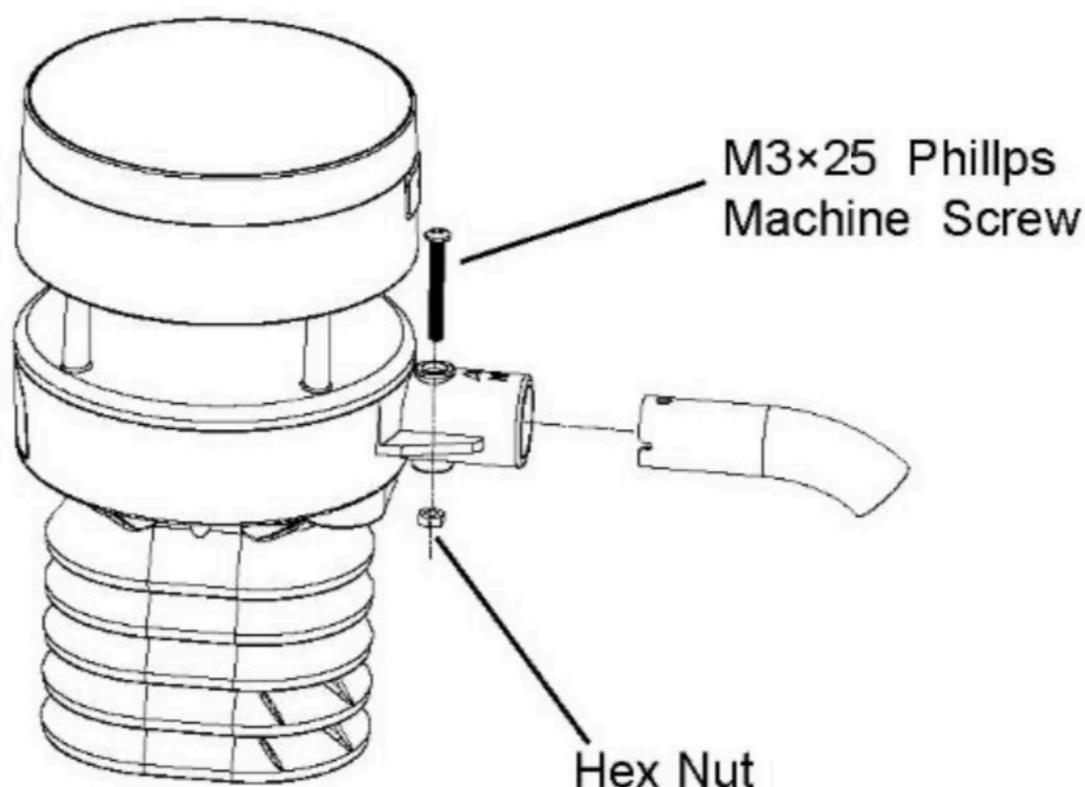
schema di montaggio del pacchetto del sensore 5-3
